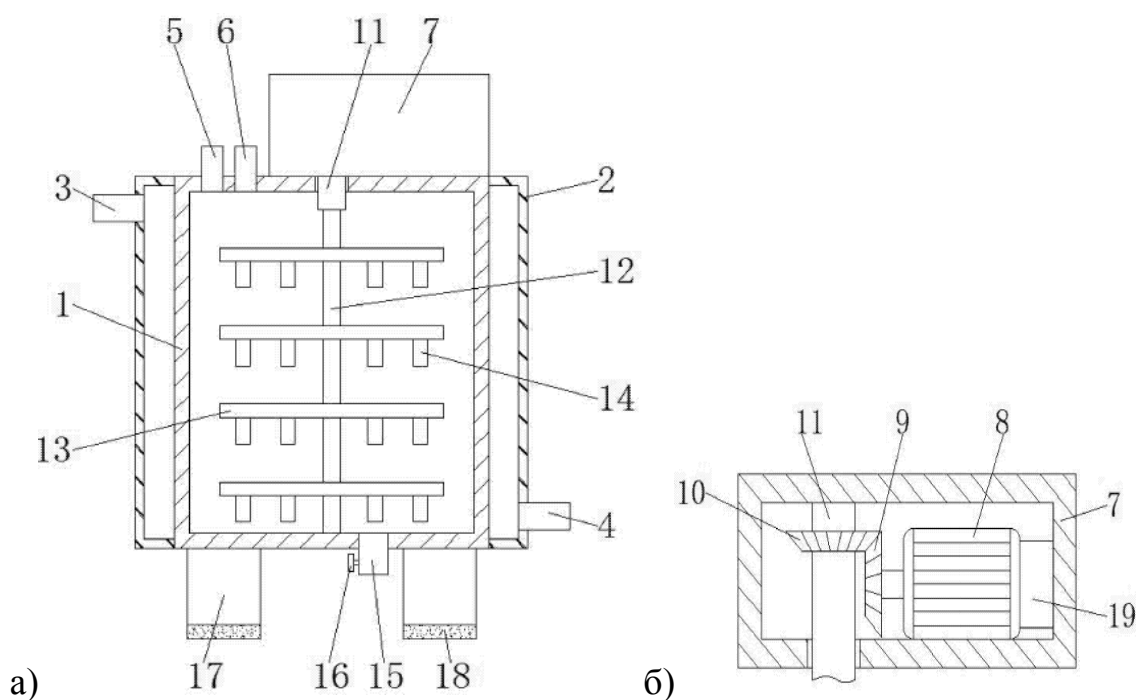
Схема реактора алкилювання з рухомим шаром
